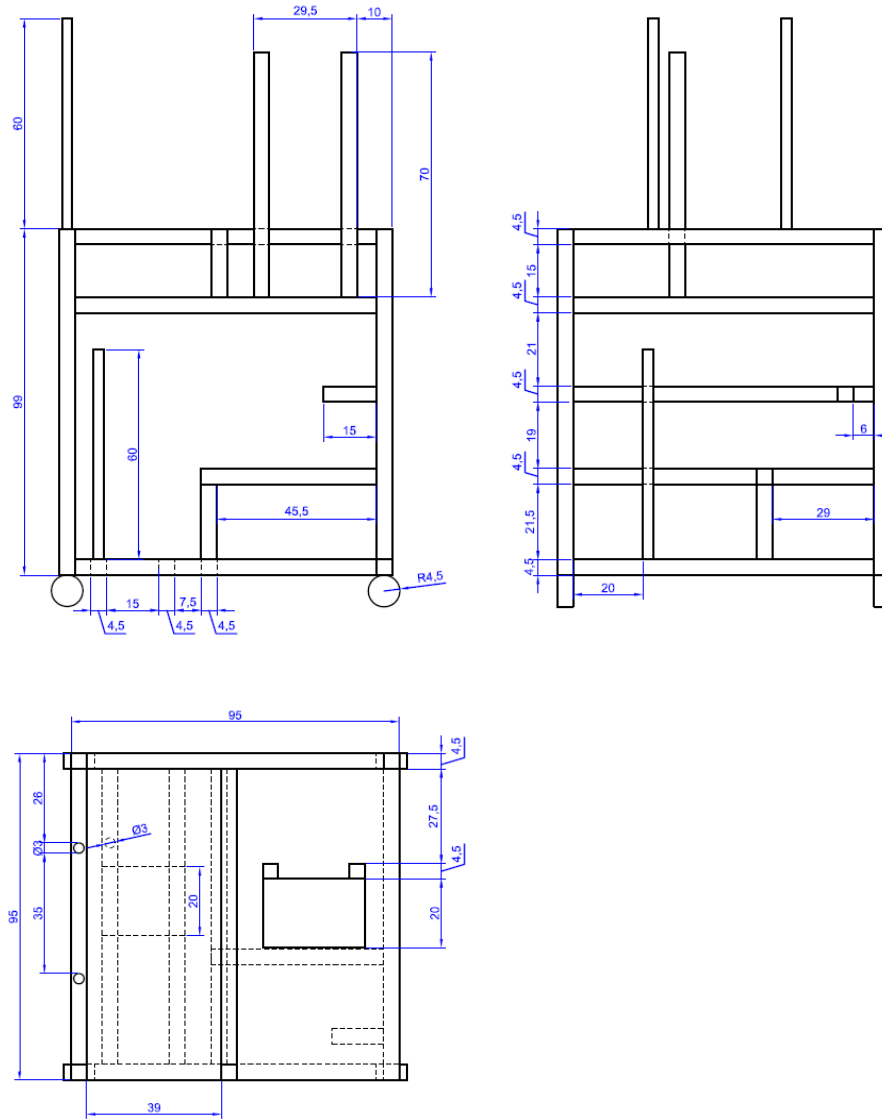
Alzado, planta y perfil con acotaciones en cm de la estructura metálica de la planta piloto de UF 3. (AutoCAD).
